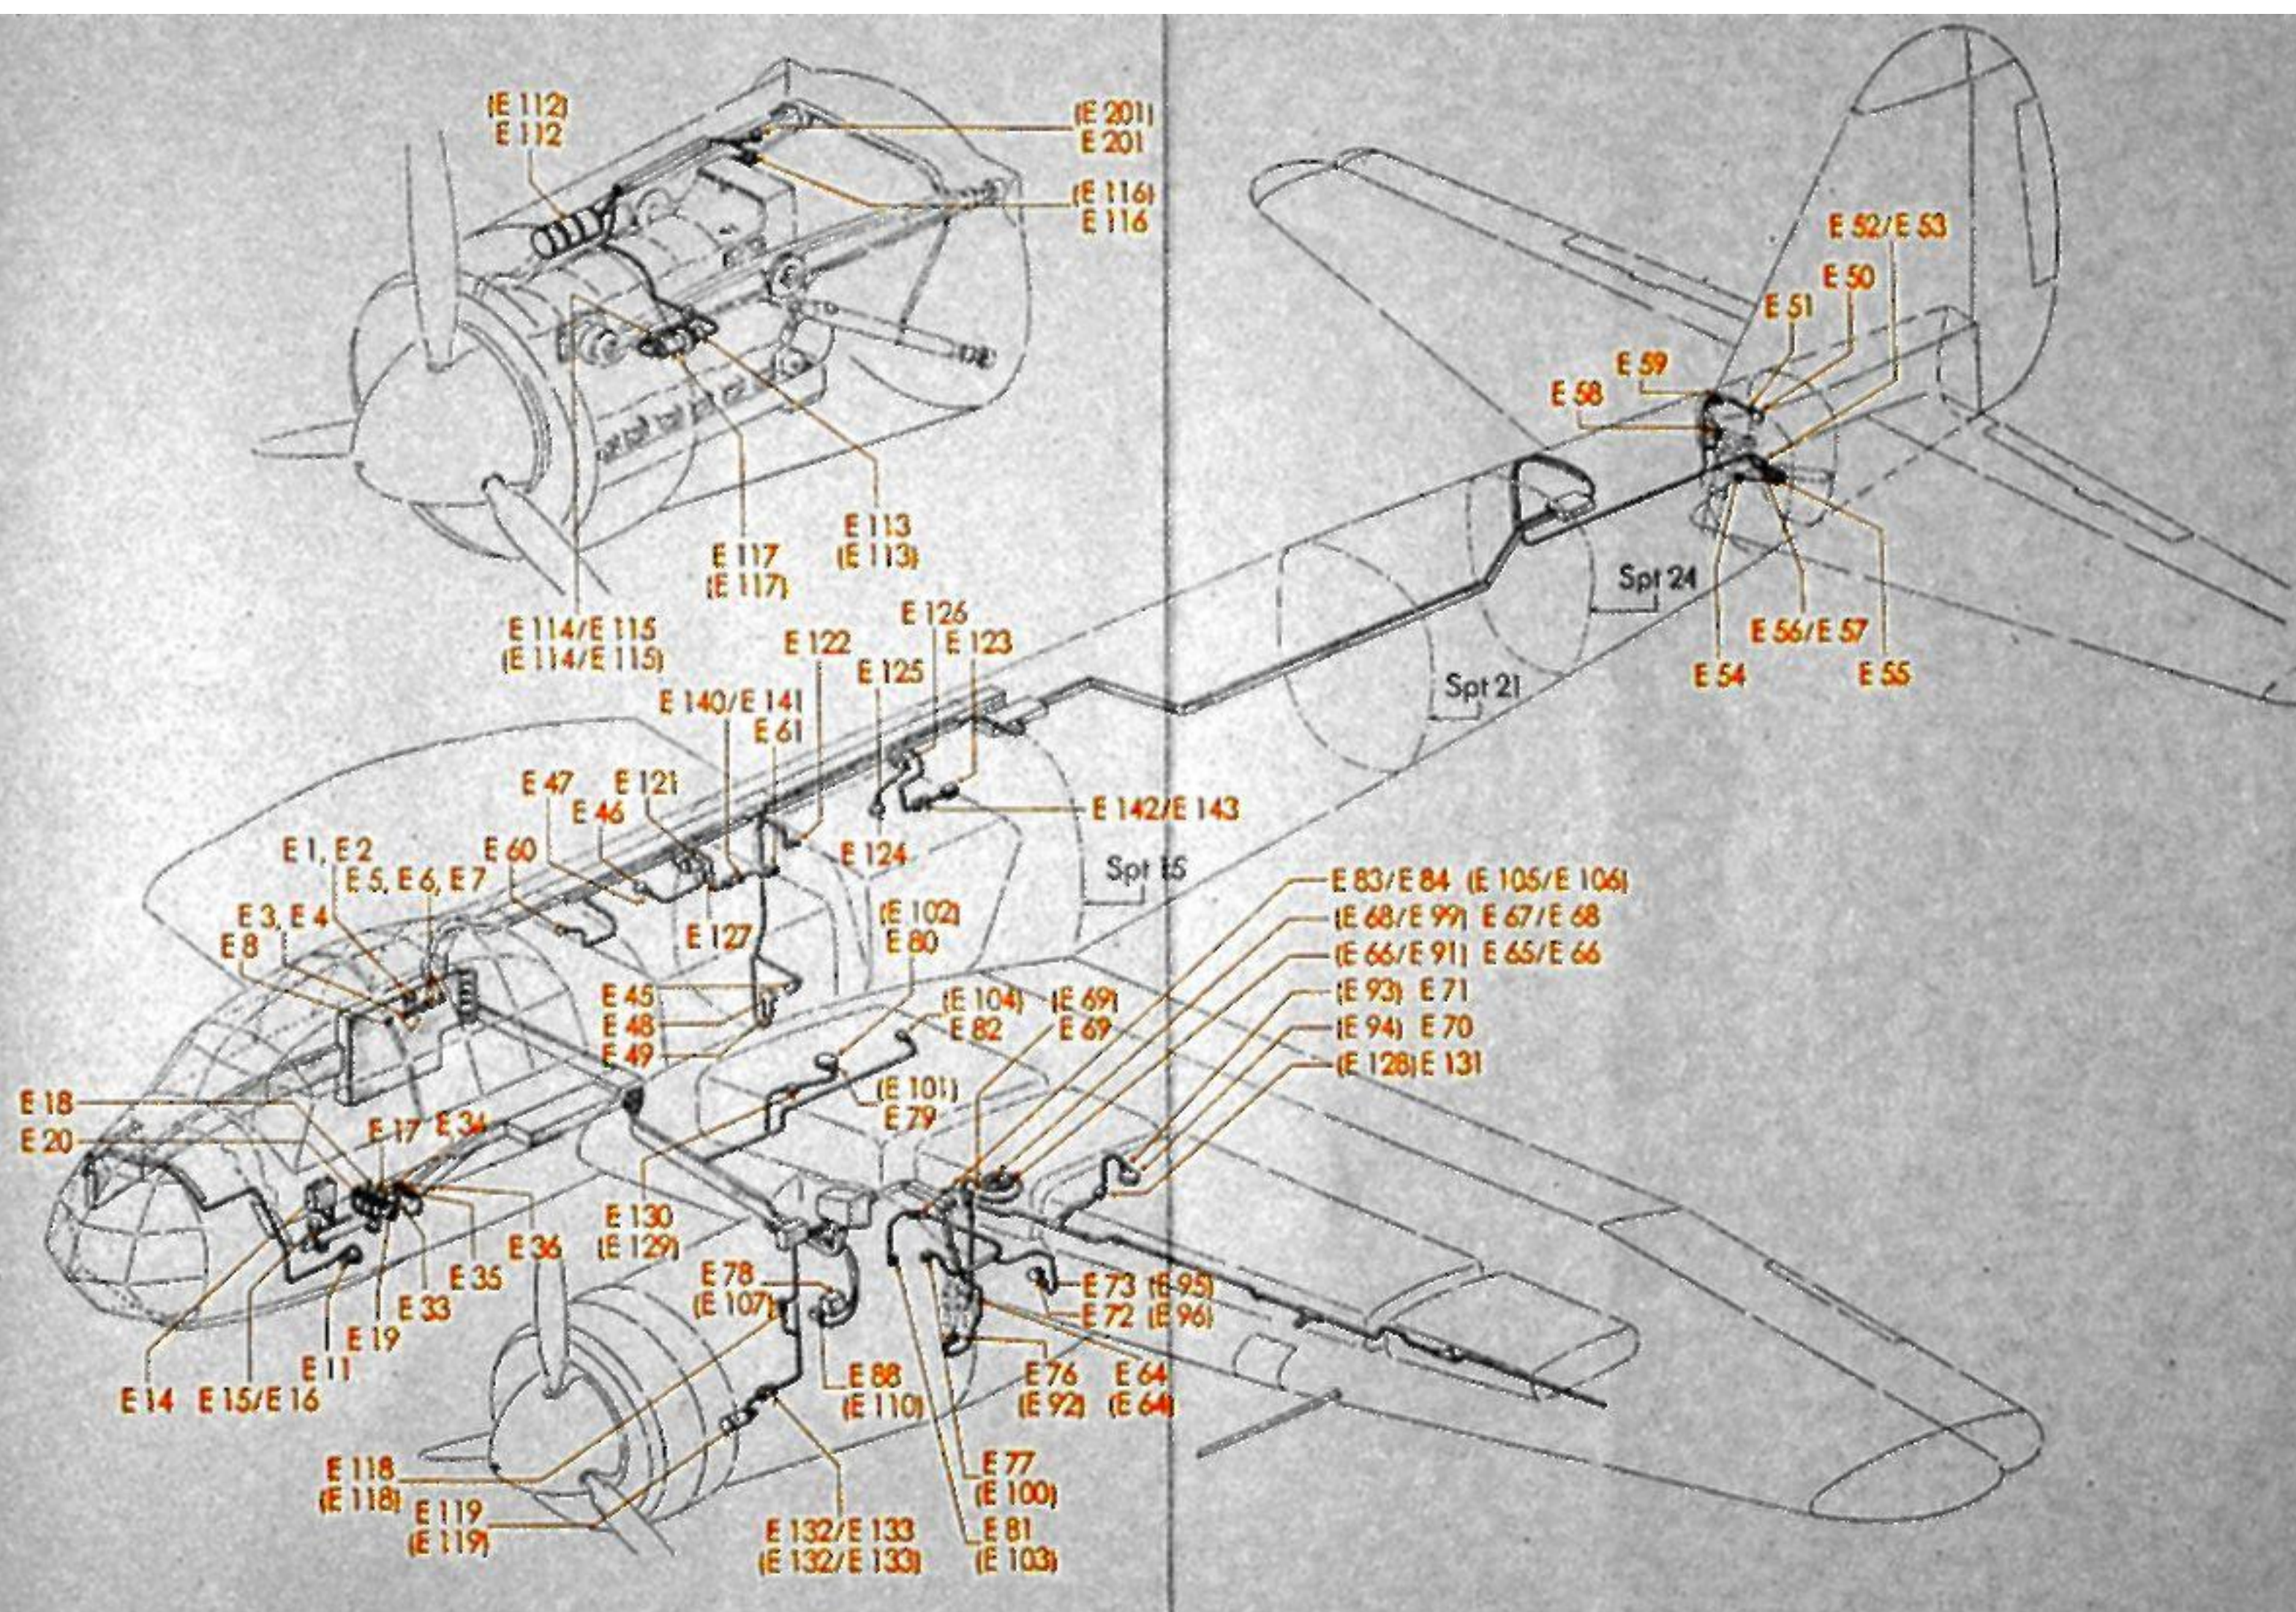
Lageplan der elektrischen Antriebe / E-Anlage
